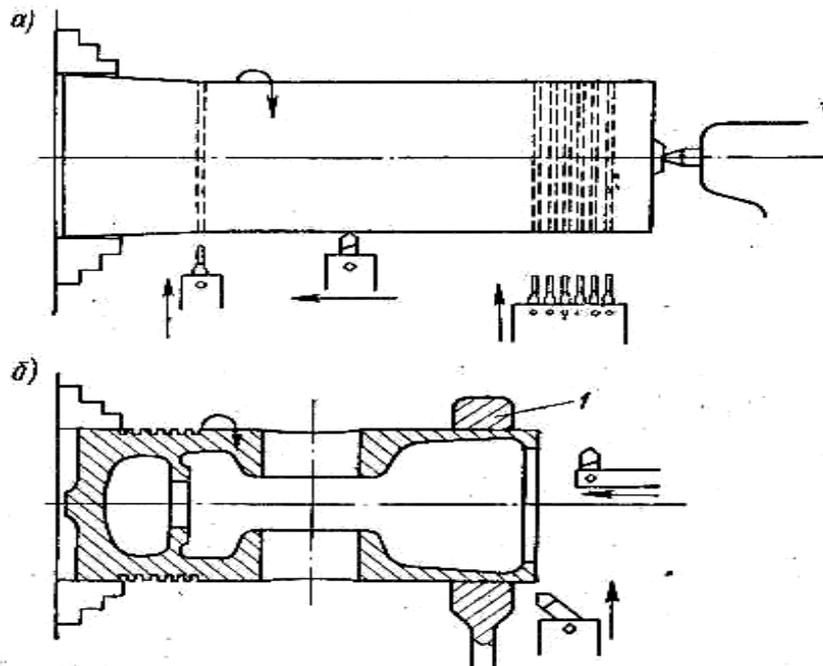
Черновая обточка и расточка поршня большого размера
